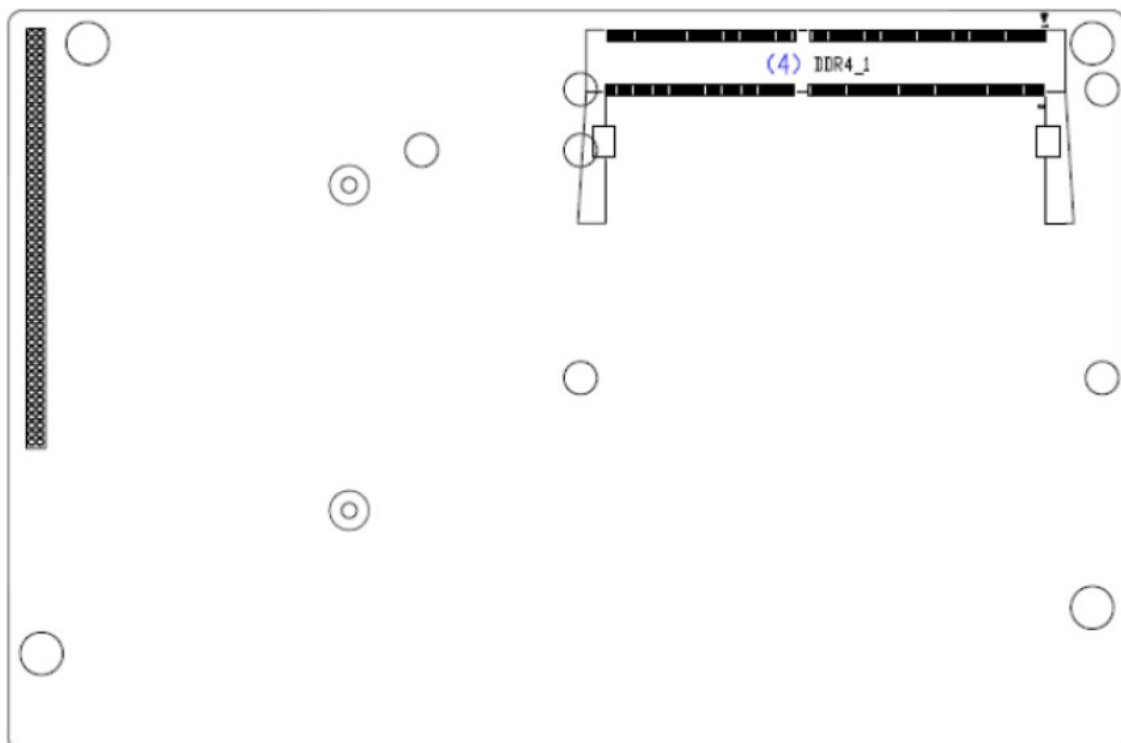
SBC-7114 - Anschlüsse und Jumper - Untersicht
